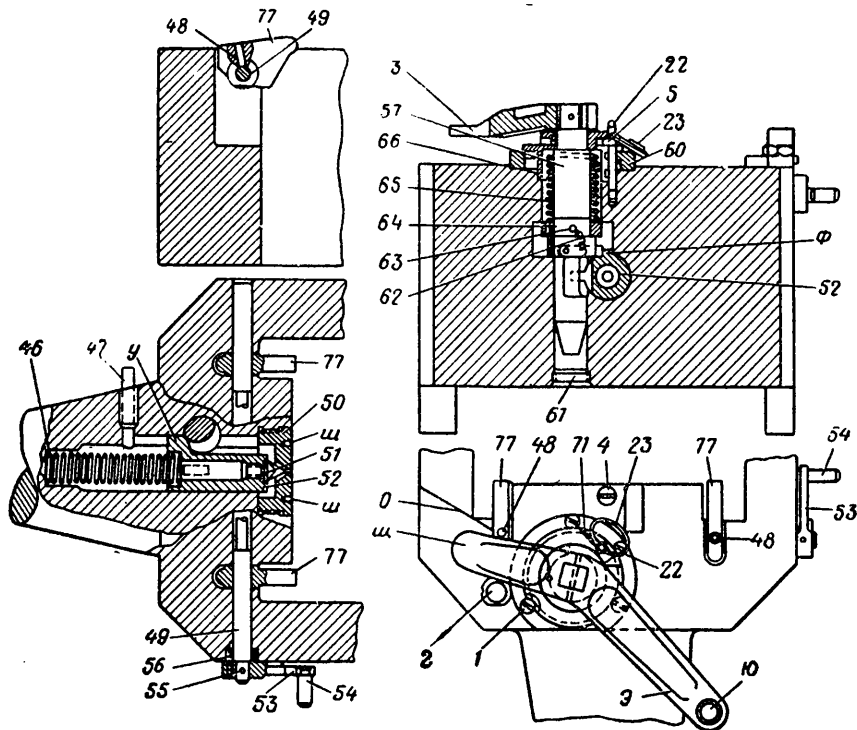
Стреляющее приспособление, собранное в казеннике (разрезы и сечения):
